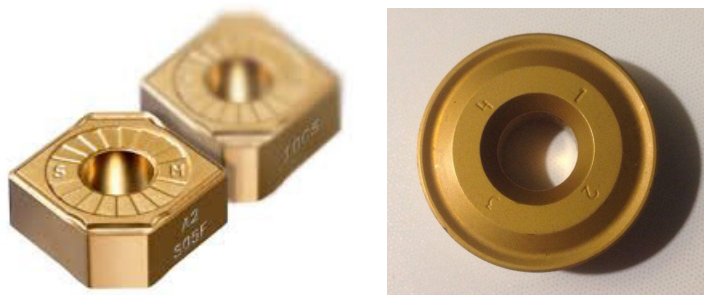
Пластины ромбические с обрезанным углом при вершине режущей кромки и круглые
